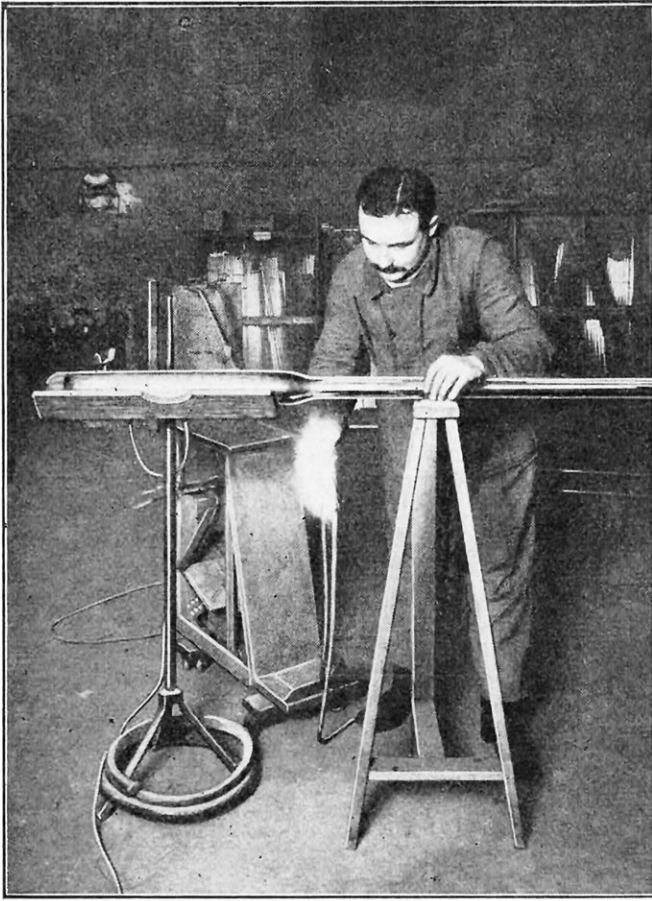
LA SOUDURE D'UNE ÉLECTRODE A UN TUBE
